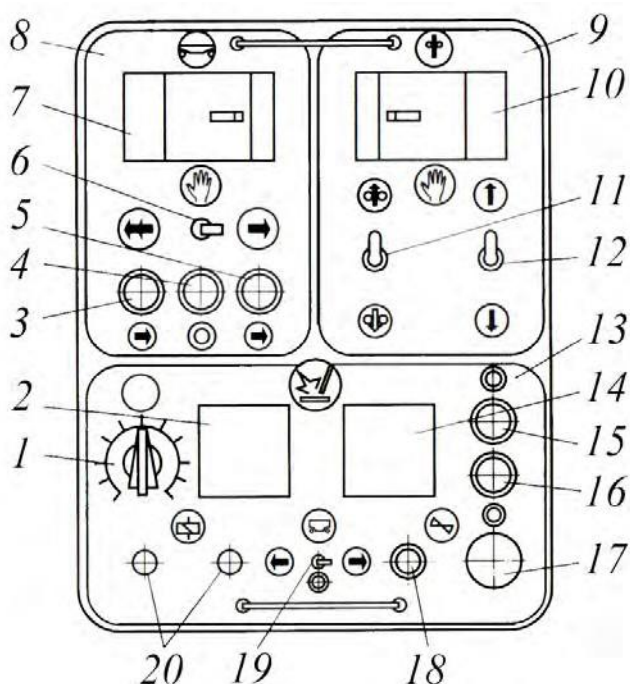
Панель управления сварочного автомата А-1416
